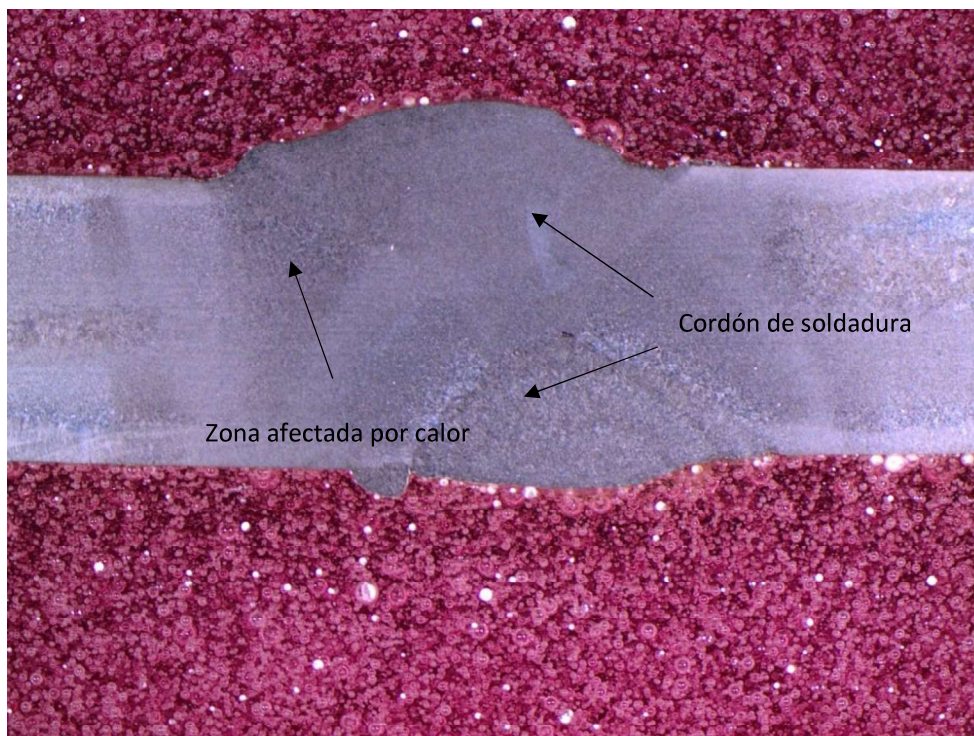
Macrografía probeta soldada con acero cementado como material base.
